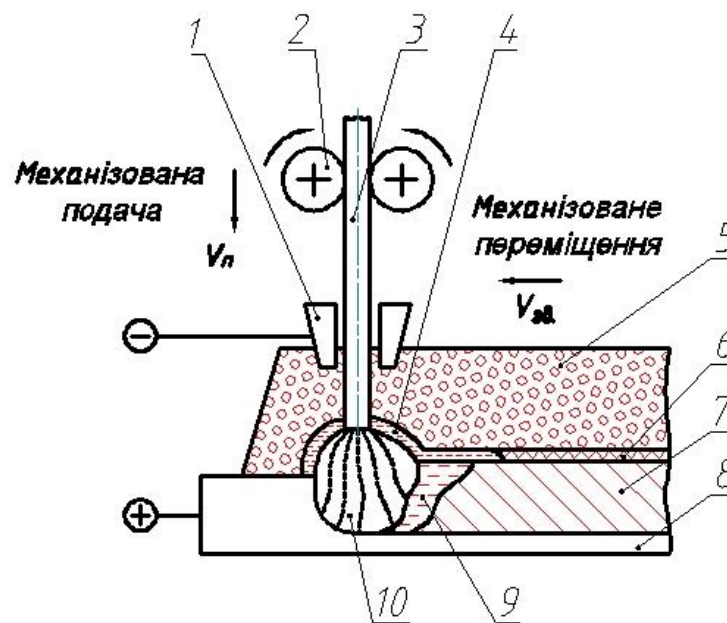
Схема автоматичного дугового зварювання під флюсом
